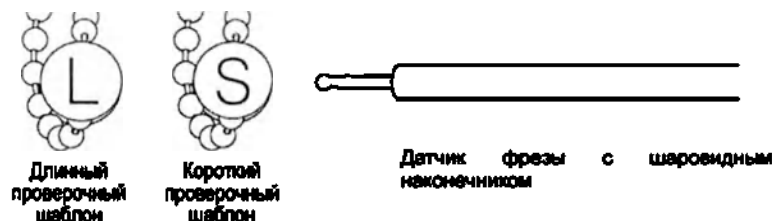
Измерители для проверки установки датчика шаровидной фрезы
